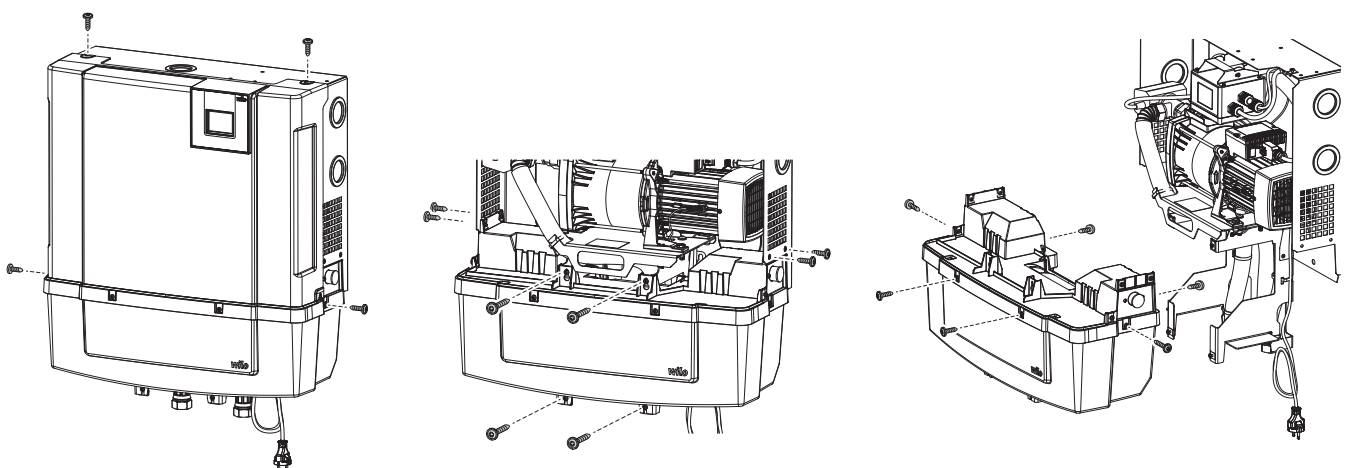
Desserrage des vis du couvercle de l'appareil, desserrage des vis de fixation de la cuve sur le châssis, retrait de la cuve avec la vanne de réalimentation et desserrage des vis du couvercle de la bêche de stockage
